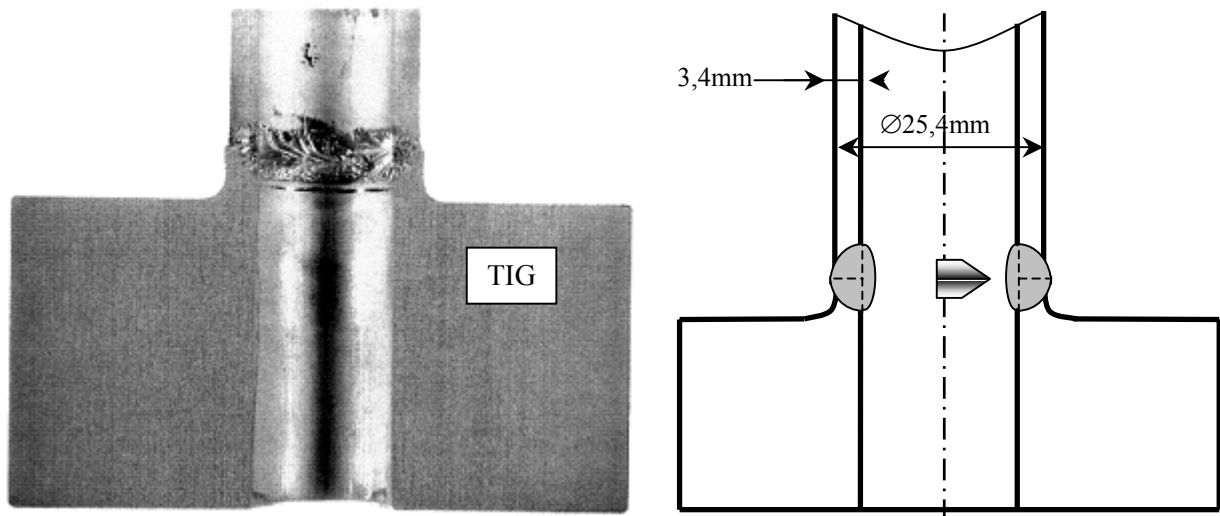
Soudage TIG tube sur plaque d'acier 304L en intérieur tube - courant pulsé 150/130A
